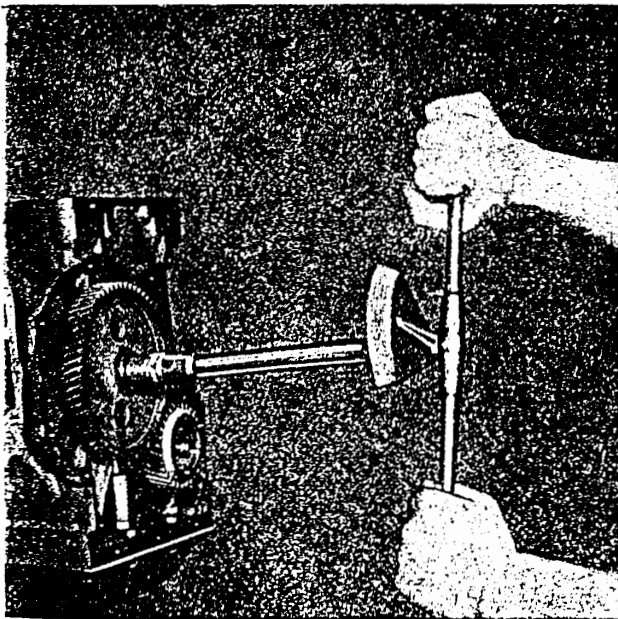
Befestigungsschraube des Nockenwellenrades mit Drehmomentschlüssel 40 Nm (4 kpm) anziehen, dabei Arretierung gegen das Durchdrehen des Motors, Werkzeug Nr. 324.020-M 114 verwenden.
